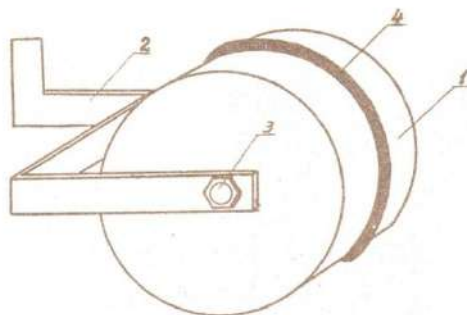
Каток-бороздодел с продольными и поперечными выступами: 1-корпус, 2-вилка, 3-ось, 4-продольный выступ.
